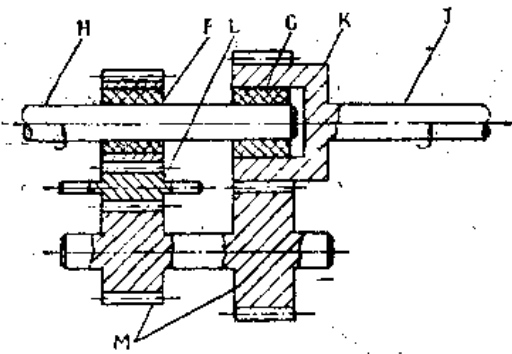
与图18-7所示的伞齿轮装置有相同作用的正齿轮装置
